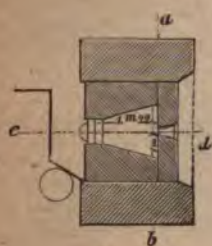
Grundriß nach gh. Einfacher Schachtofen.
